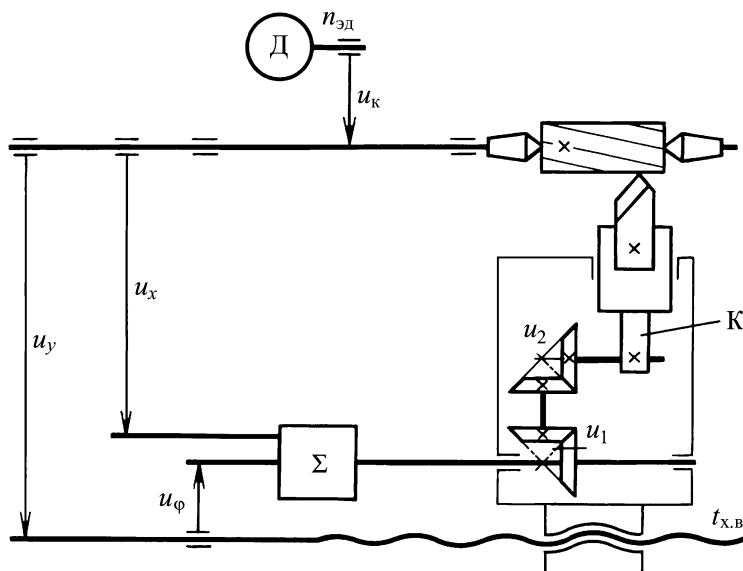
Кинематическая схема затылования цилиндрических фрез со спиральными стружечными канавками
